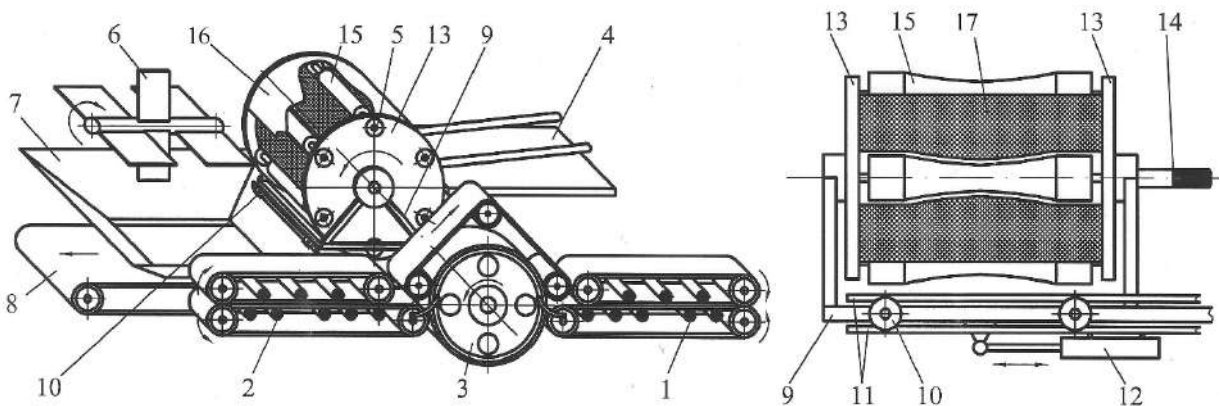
Пристрій для обробки верхівкової частини стрічки льону: 1, 2 – затискні транспортери; 3 – дисковий затискний транспортер; 4 – підвідний стіл; 5 – барабан; 6 – струшувач; 7 – накопичувач; 8 – вивантажувальний транспортер; 9 – рухома рама; 10 – ролики; 11 – спрямовувачі; 12 – гідроциліндр; 13 – диски; 14 – приводний вал; 15 – вальці; 16 – опорна поверхня; 17 – вставки [104]
